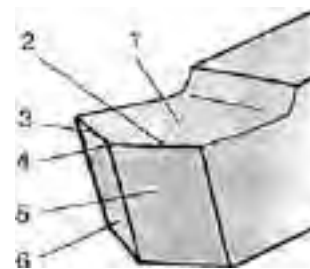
ЕЛЕМЕНТИ ГОТОВКИ РІЗЦЯ
